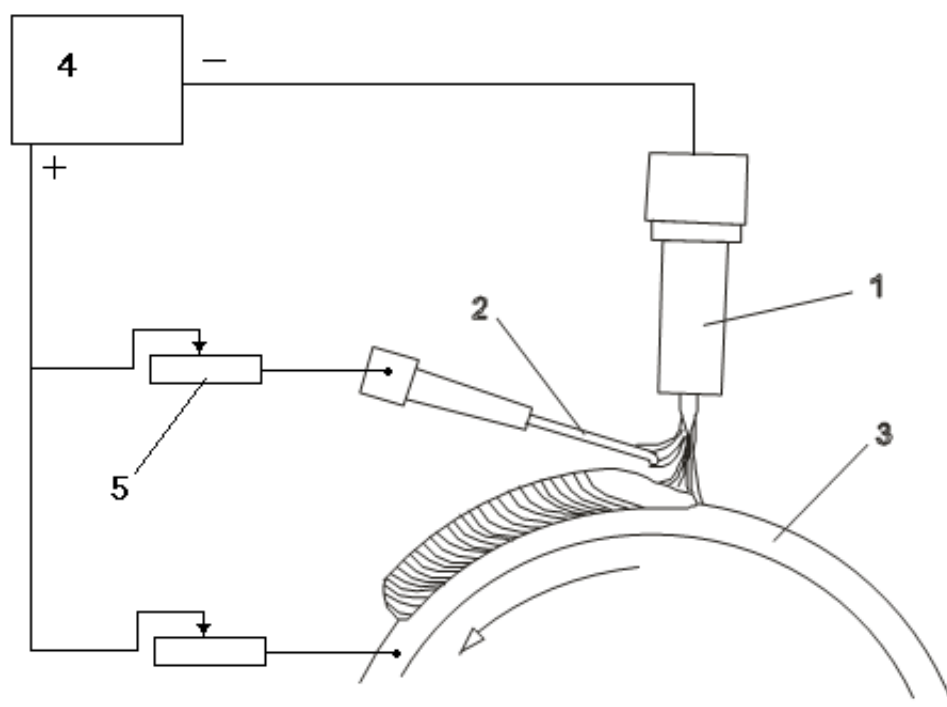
Схема питания двойной свободной дугой при сварке цилиндрических деталей: 1-горелка , 2 присадочная проволока, 3 цилиндрическое изделие, 4- источник питания, 5- балластный реостат.
